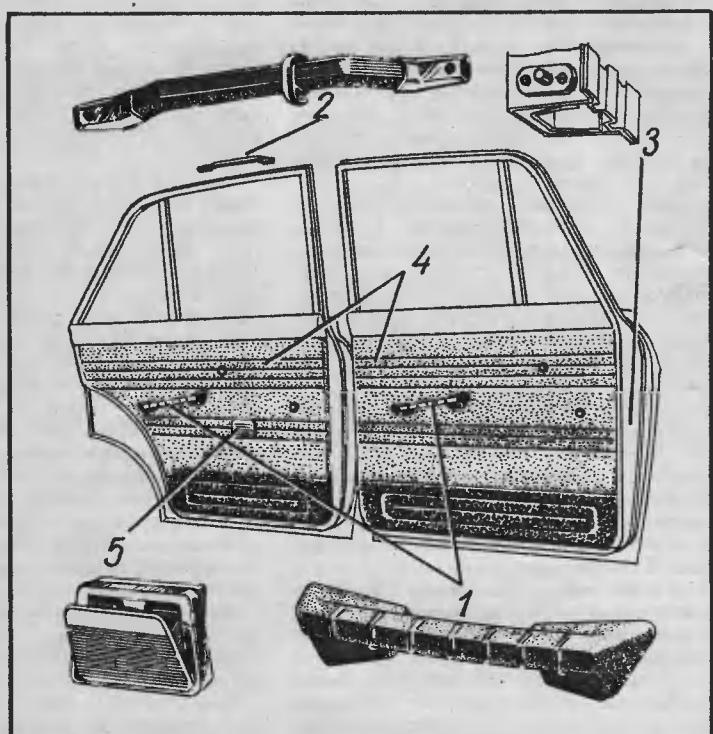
Внутренние детали: 1 — подлокотники; 2 — поручни дверей; 3 — подлокотники для одежды; 4 — пепельница; 5 — обивка дверей
